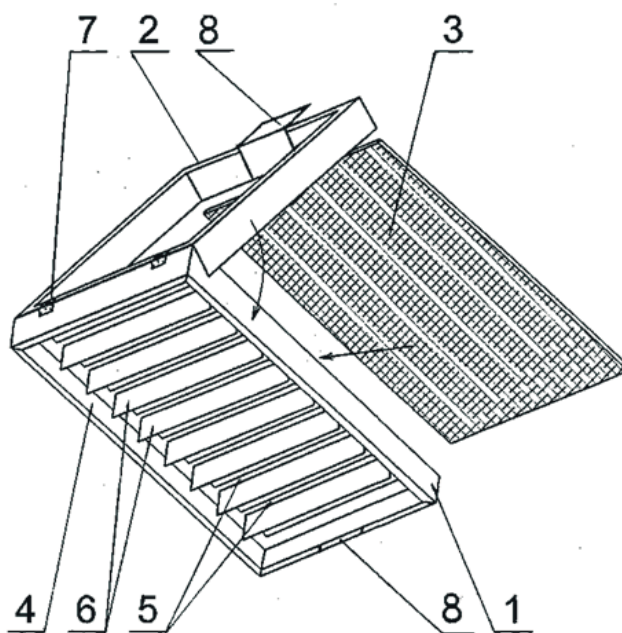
Корпус воздушного фильтра: 1 – несущая рамка; 2 – прижимная рамка; 3 – фильтрующий материал; 4 – боковые поверхности; 5 – прижимные пластины; 6 – направляющие планки; 7 – шарнирное соединение; 8 – магнитные крепления
